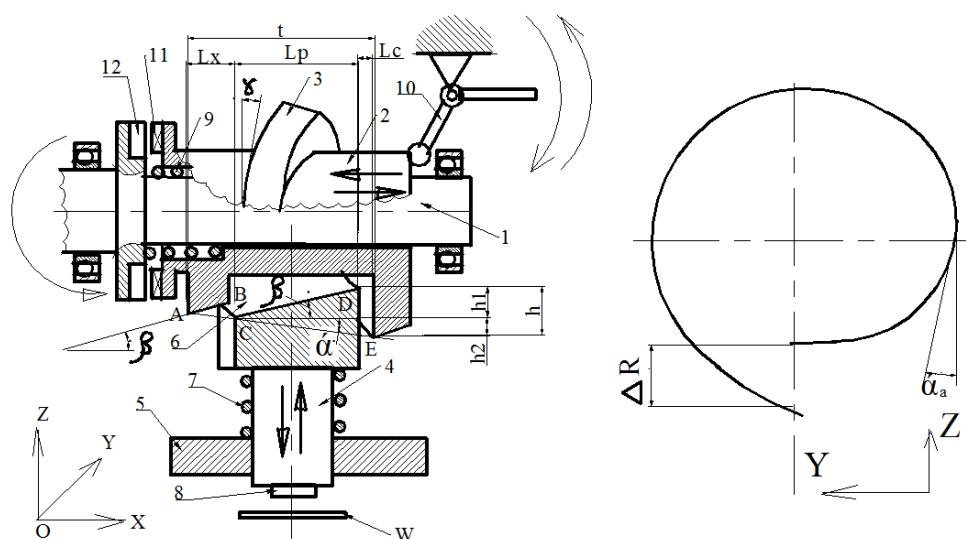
Схема механизма кулачкового-винтового пресса. 1 – вал, 2 – цилиндр, 3 – коническая винтовая поверхность, 4 – ползун, 5 – корпус, 6 – вогнутая поверхность, 7 – пружина, 8 – инструмент, 9 – пружина, 10 – механизм переключения, 11,12 – кулачки муфты.
